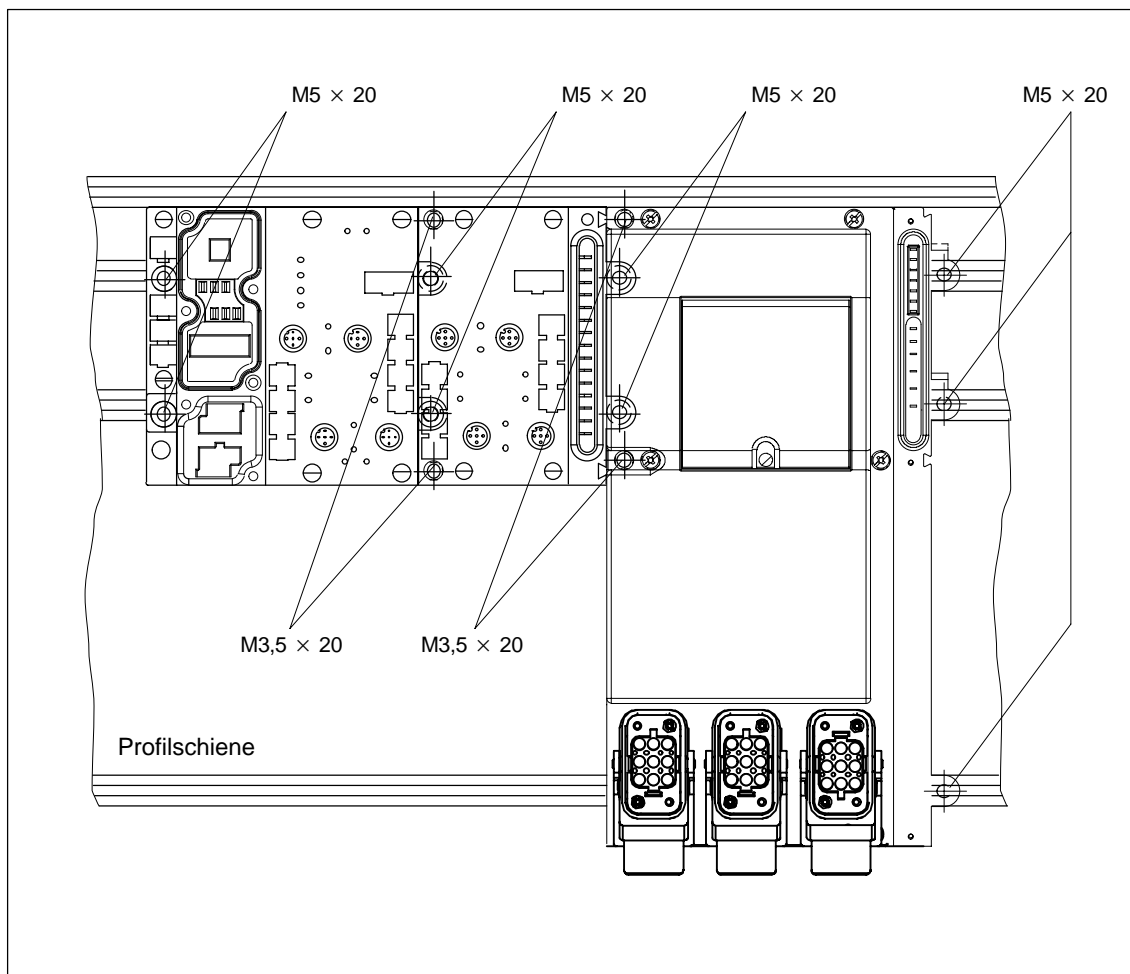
Befestigungsschrauben für Basis- und Erweiterungsmodule
